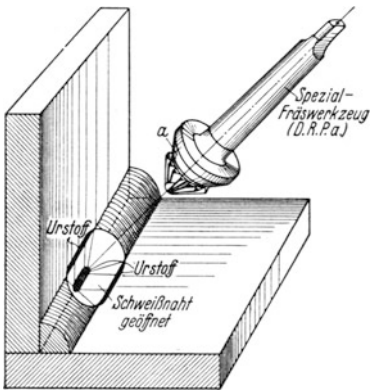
Prüfgerät für Schweißnähte nach Schmuckler.
